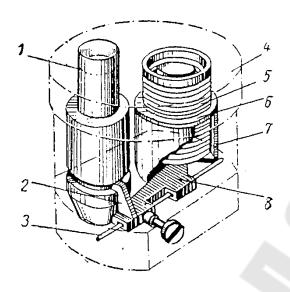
Схема термовыключателя: 1 — стержень; 2 — собачка; 3 — ось; 4 — корпус; 5 — цилиндр; 6 — кольцо; 7 — стакан; 8 — рычаг
